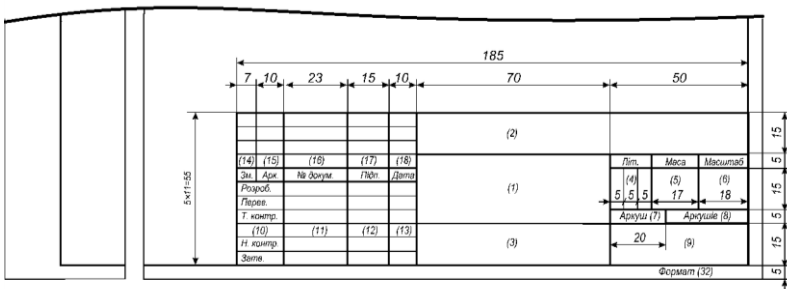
Основний напис конструкторських креслень і схем – форма 1
